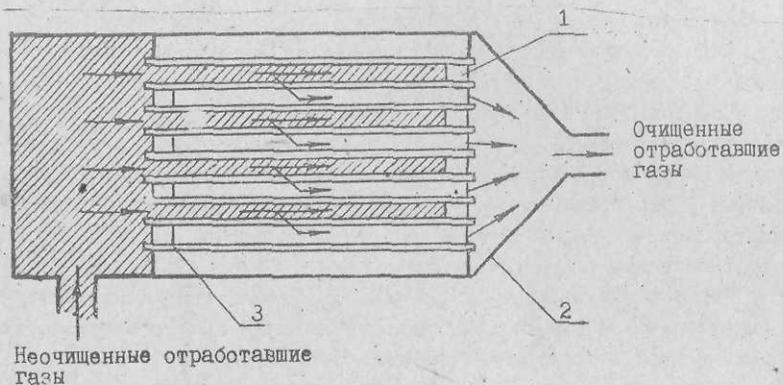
Монолитный керамический фильтроэлемент фирмы "КХД Дойтц" (ФРГ): 1 - керамические заглушки; 2 - металлический корпус; 3 - пористая керамика
